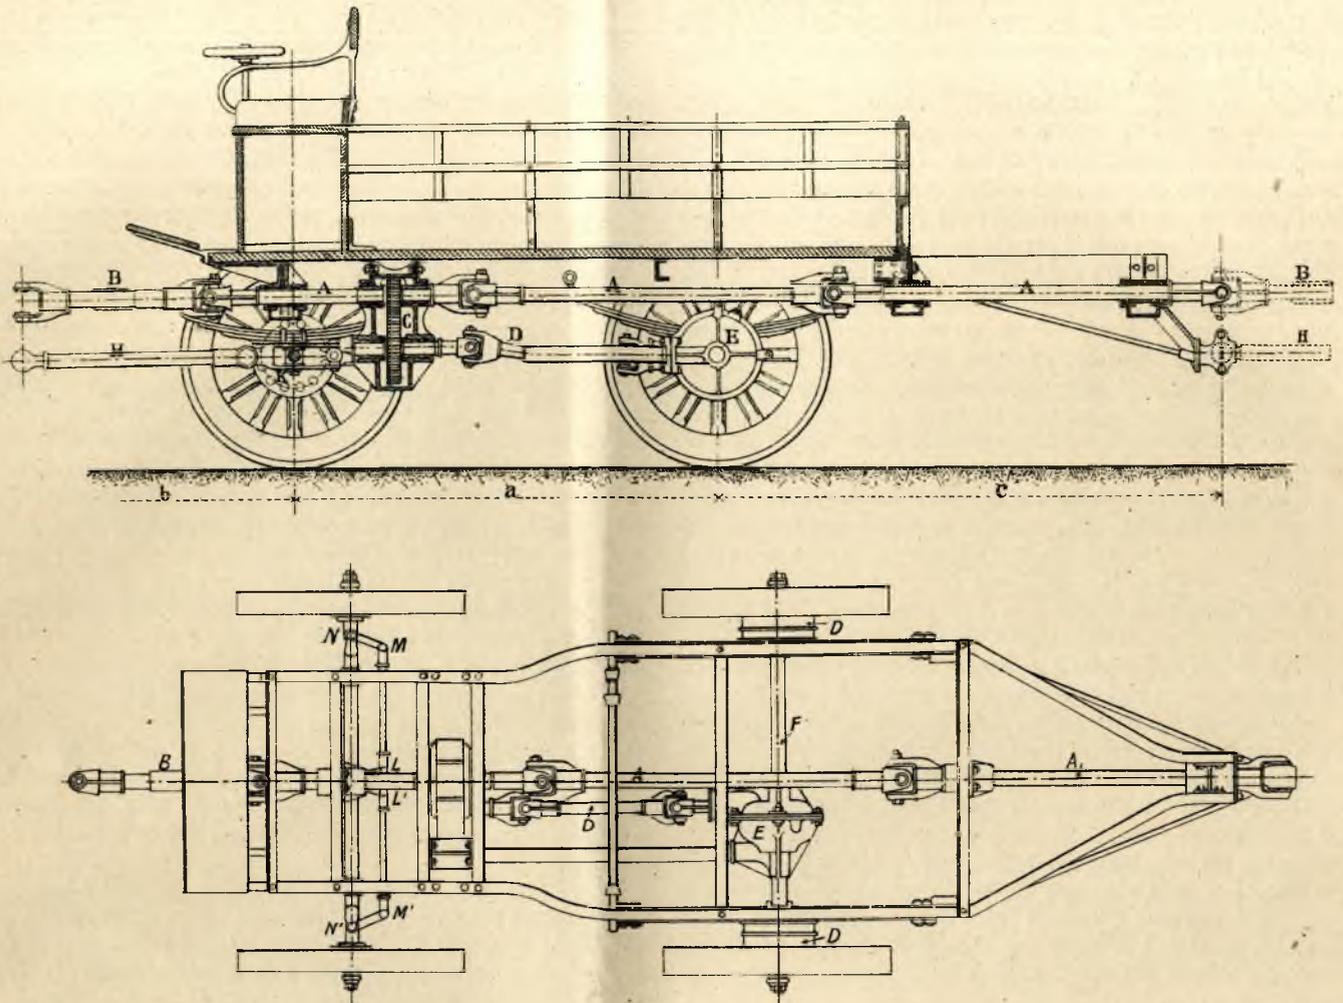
Elevazione e pianta di un carro del treno Rénard.
